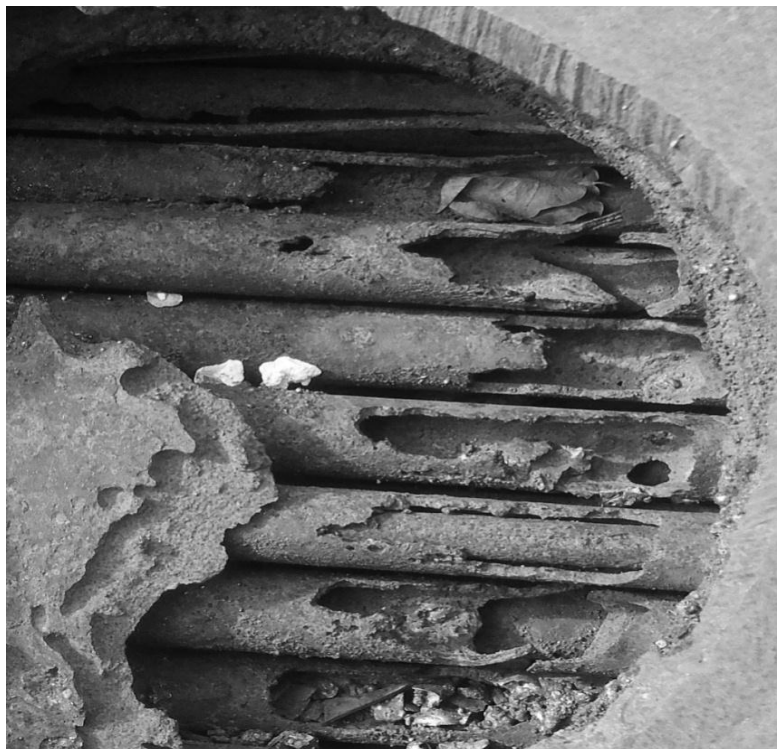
Photo montrant la corrosion avancée de la première rangée tubulaire.
